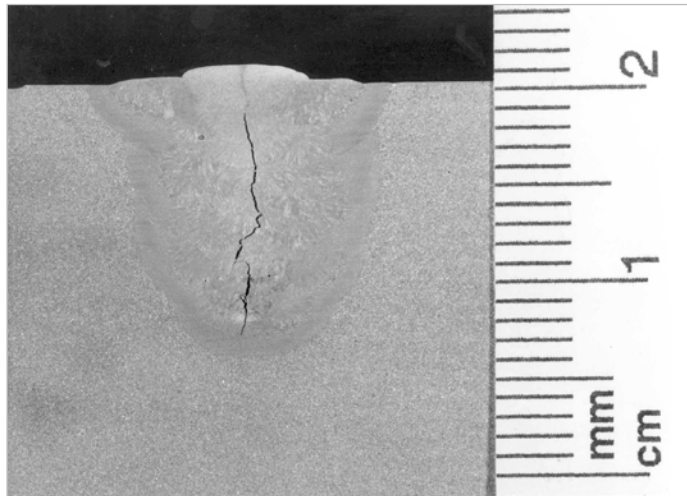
Macro de un defecto de soldadura intencionado introducido en una pieza de acero de baja aleación.
